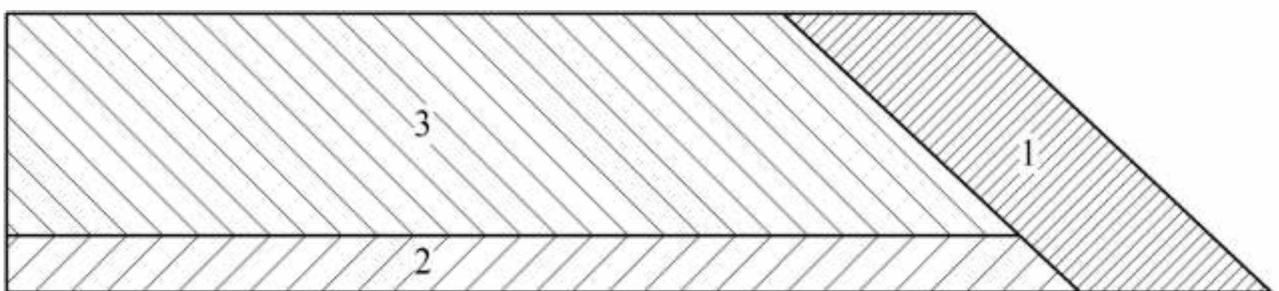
Робочі поверхні лемеша: 1 – робоча поверхня носової частини; 2 – робоча поверхня леза; 3 – робоча поверхня п'яти
